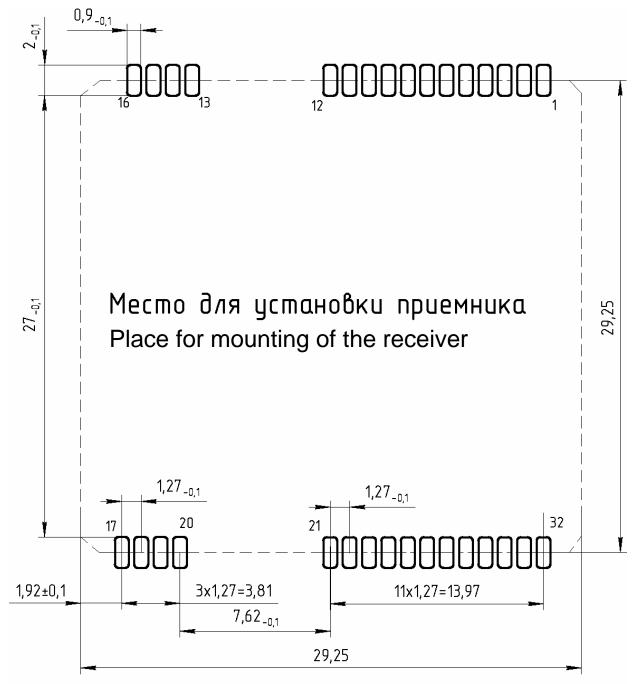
Габаритные размеры МНП-M7.1 для исполнения ЦВИЯ.468157.113-05 Figure 5 – Overall dimensions of MNP-M7.1 for modification CVIA.468157.113-05
